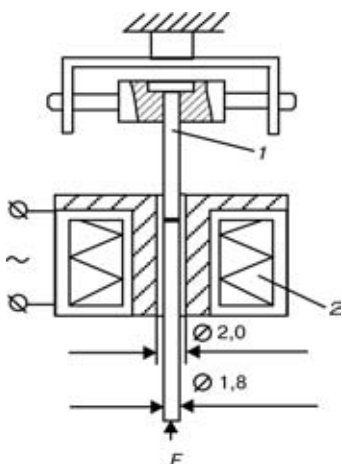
Схема нагружения паяных соединений: 1 — образцы стыкового соединения; 2 — нагреватель
